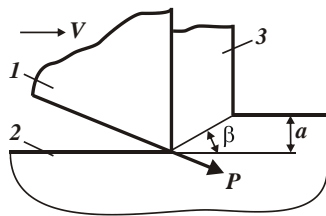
Схема розрахунку умовного кута зсуву оброблюваного матеріалу: 1 – різець; 2 – оброблюваний матеріал; 3 – стружка
